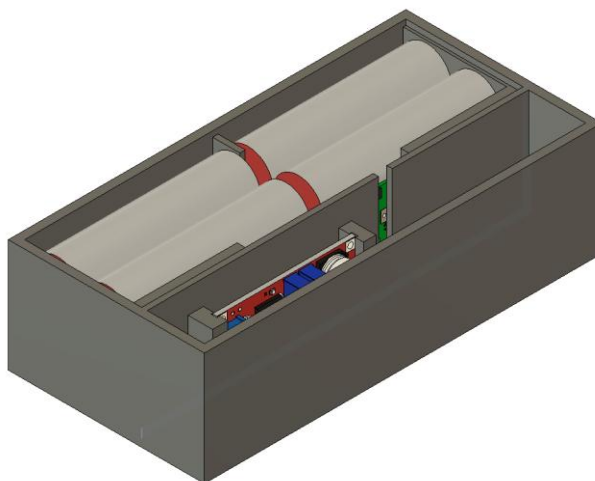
Формування зовнішніх стінок корпусу
